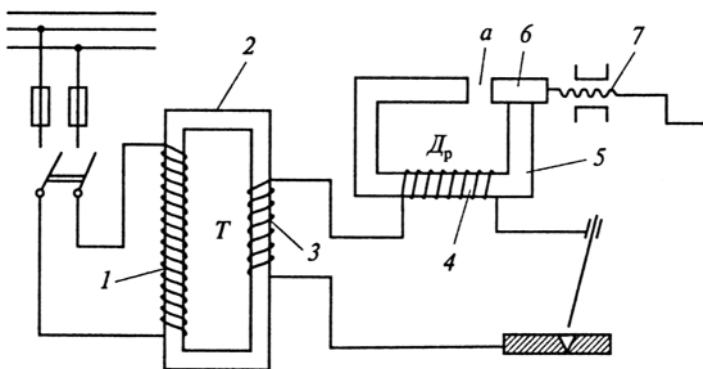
Схема сварочного трансформатора с отдельным дросселем: 1, 3 — соответственно первичная и вторичная обмотки; 2 — сердечник; 4 — обмотка дросселя D_p ; 5, 6 — соответственно неподвижная и подвижная части сердечника; 7 — винтовое приспособление; a — зазор
